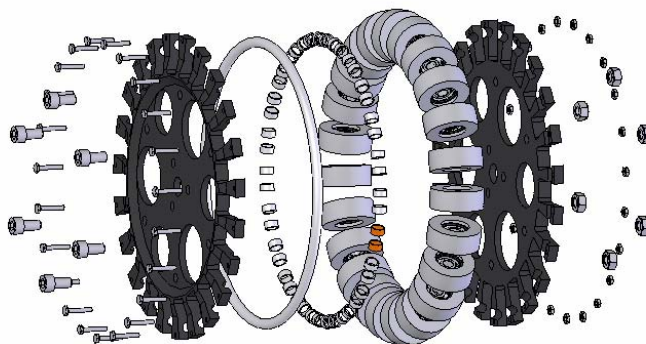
NuBot 全向轮 CAD 爆炸图
